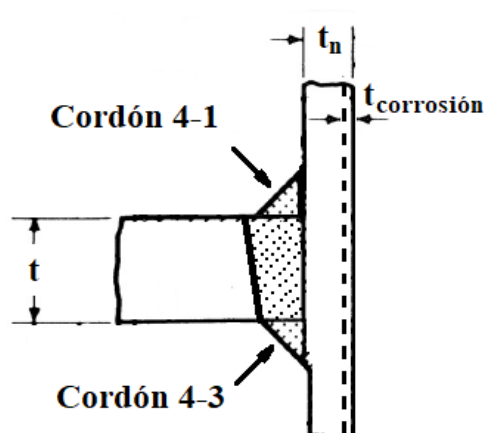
Detalle cordones de soldadura niple-cabezal de descarga de segunda etapa.
